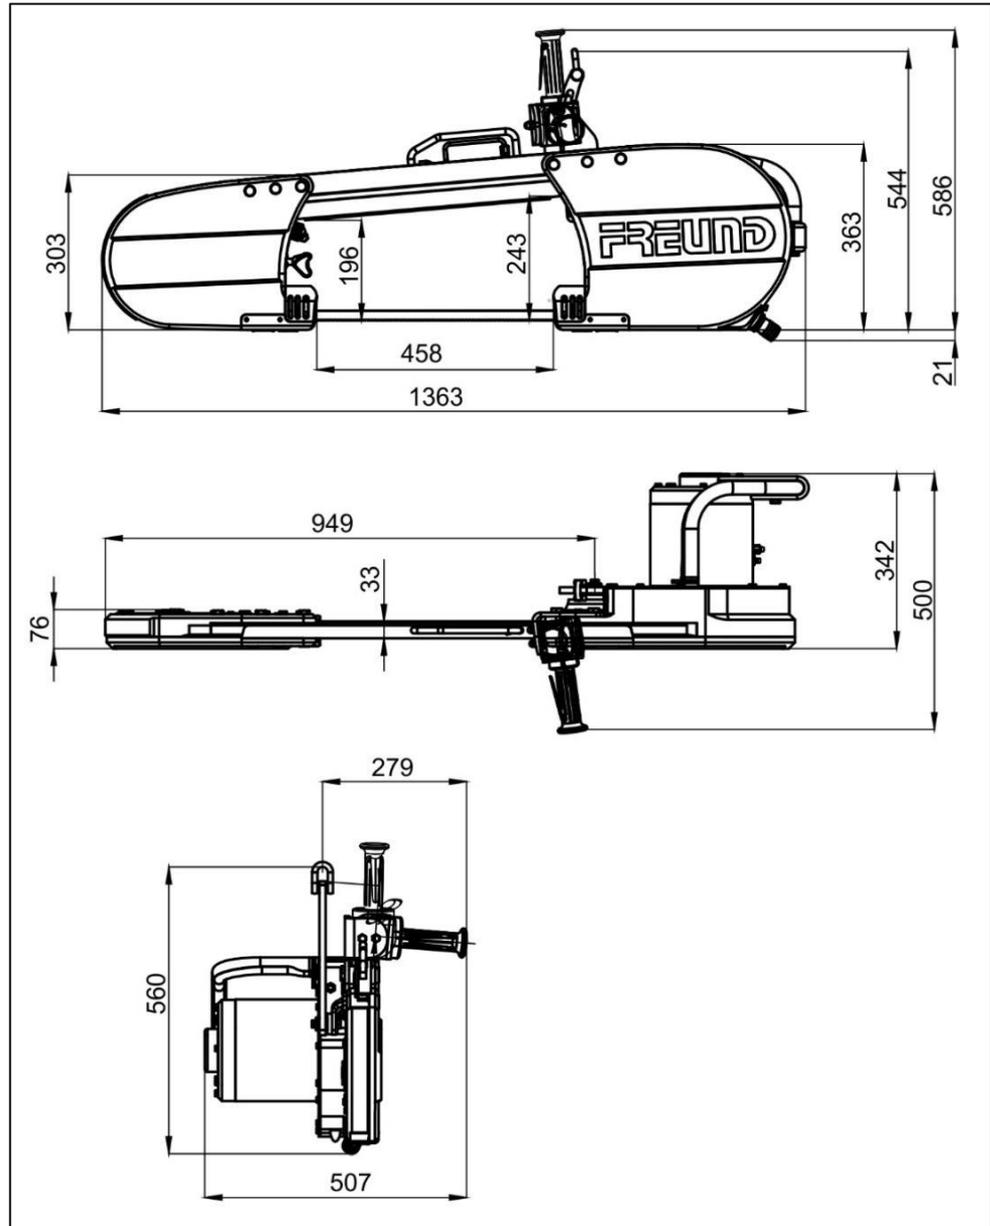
Dimensions de la scie de découpe à ruban (en mm)
